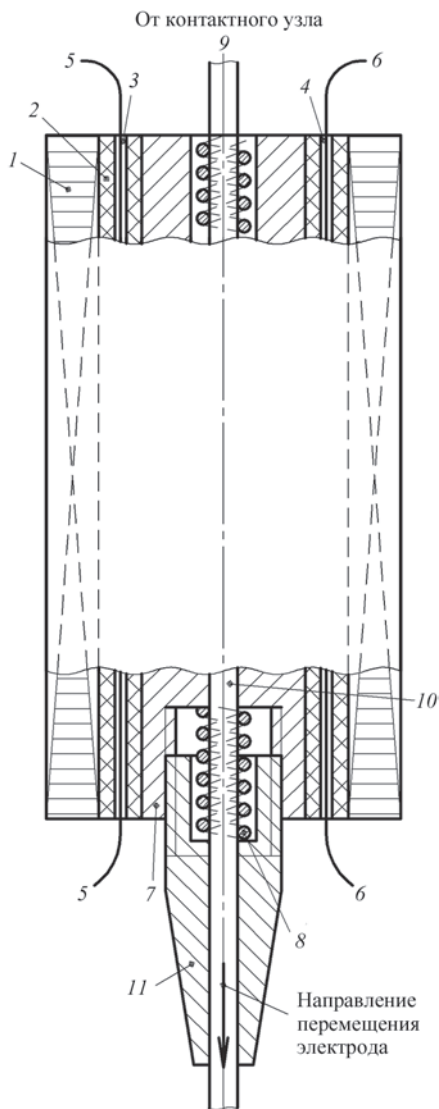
Вариант конструктивной схемы выходного импульсного трансформатора возбудителя-стабилизатора для механизированной сварки плавящимся электродом (электродной проволокой) (обозначения см. в тексте)
